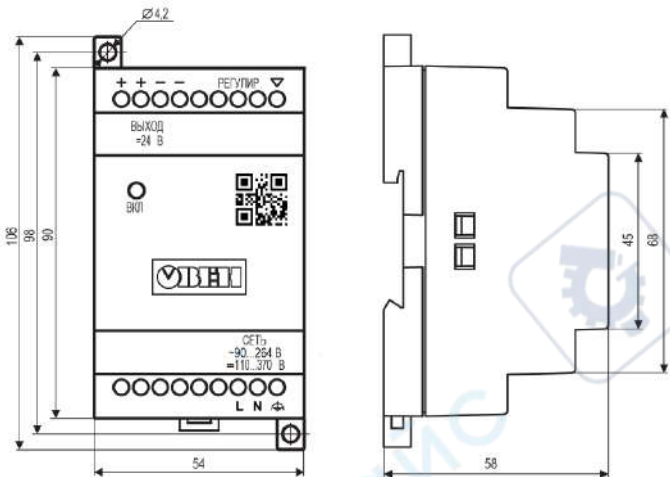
Внешний вид, габаритные и установочные размеры прибора
